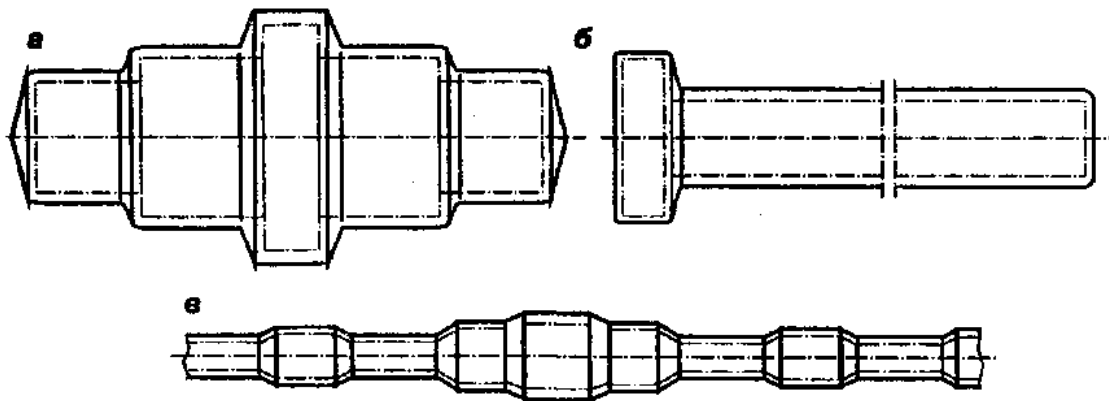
Заготовки, полученные различными методами: а – штамповкой в штампах; б – штамповкой на горизонтально-ковочной машине; в – поперечно-винтовой прокаткой
